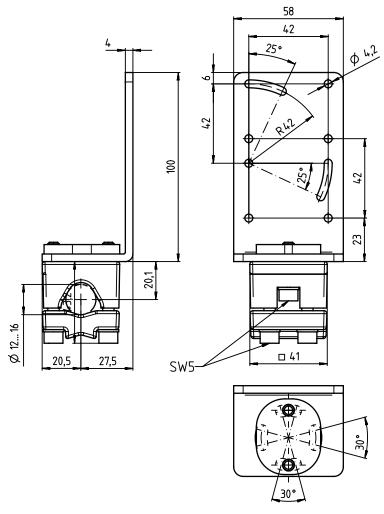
Encombrement de la pièce de fixation BT 300-1
